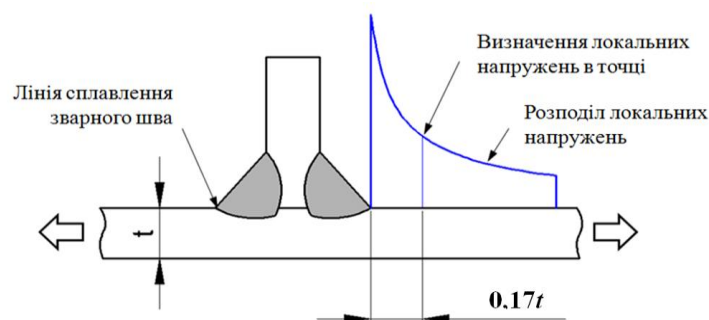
Схема визначення локальних напружень в зоні зварного з'єднання
